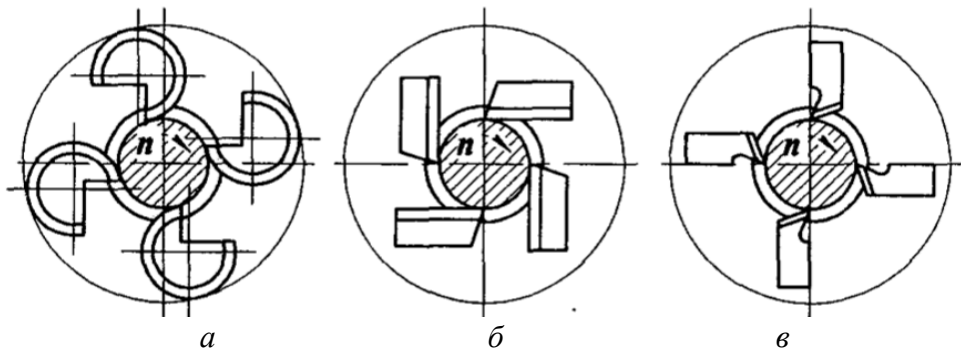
Схема роботи різьбонарізних головок: *а* – з круглими гребінками;
